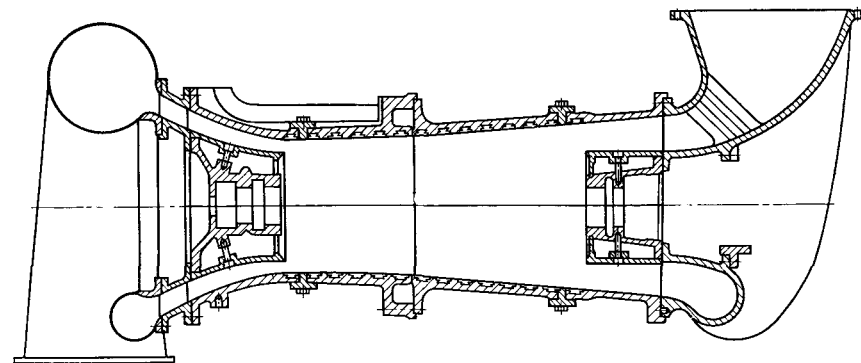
Корпус компрессора ГТУ ТА с разъемной средней частью и неразъемными патрубками фирмы Рустон
